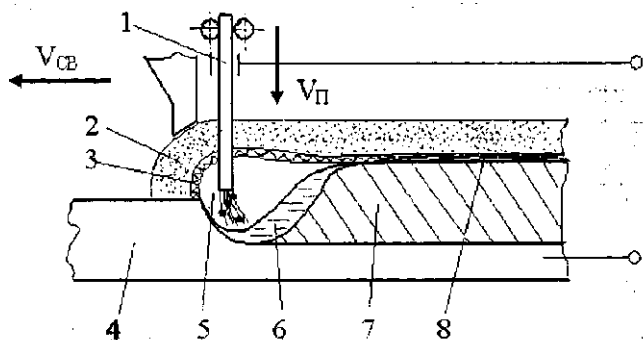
Схема процесу автоматичного зварювання під флюсом
